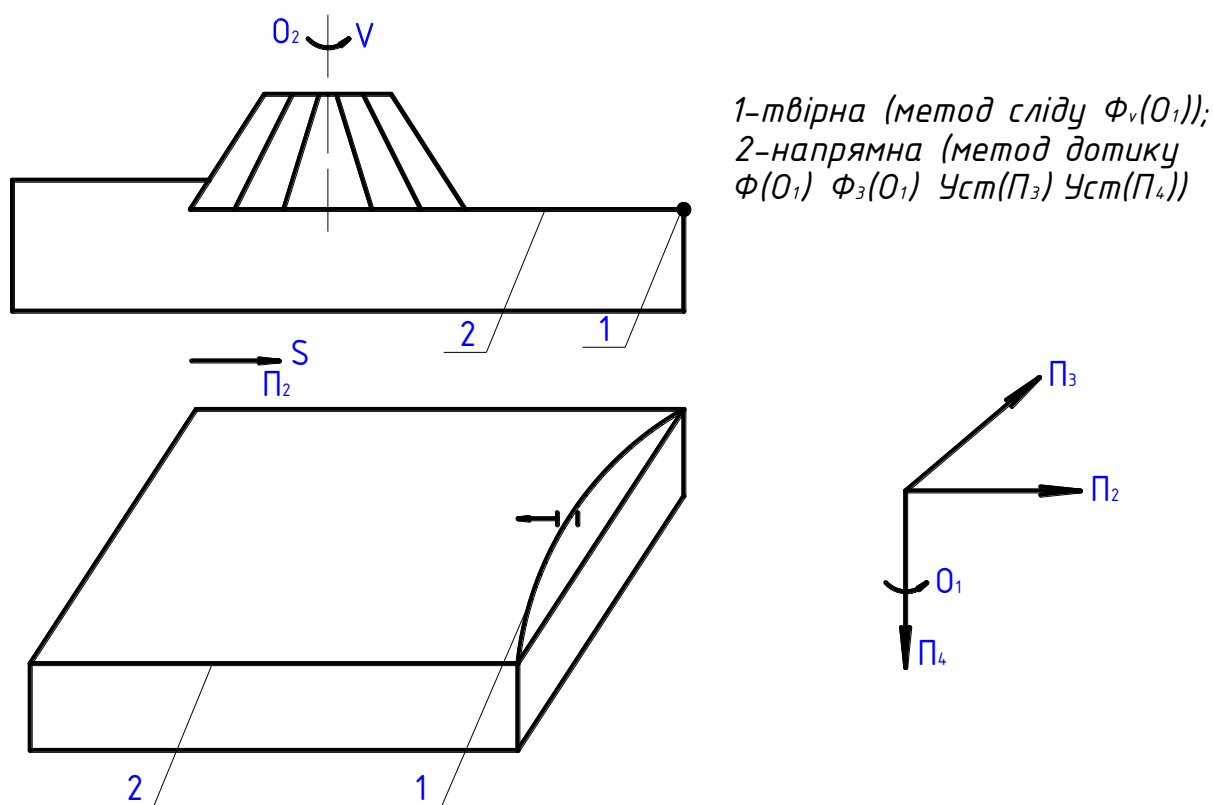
Рух інструменту при фрезеруванні торцевою фрезою.
